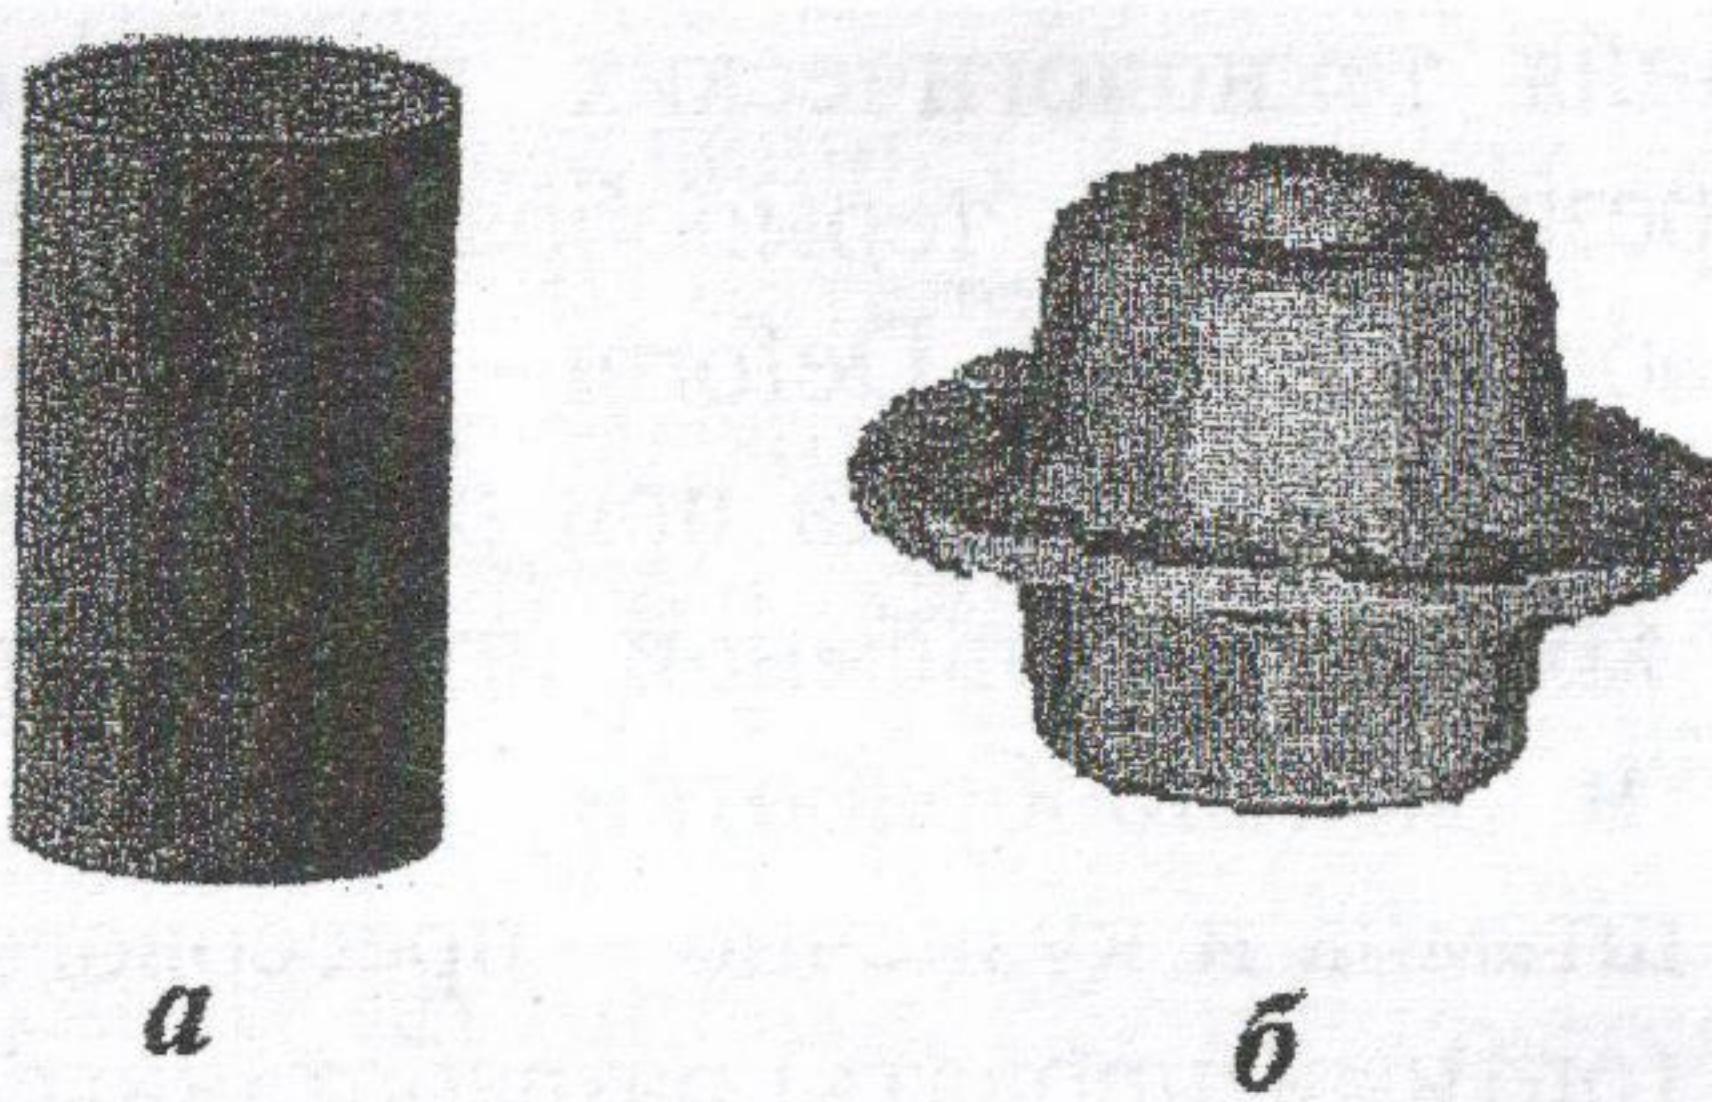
Вид (модель) исходной заготовки (а) и поковки с облоем (б)
